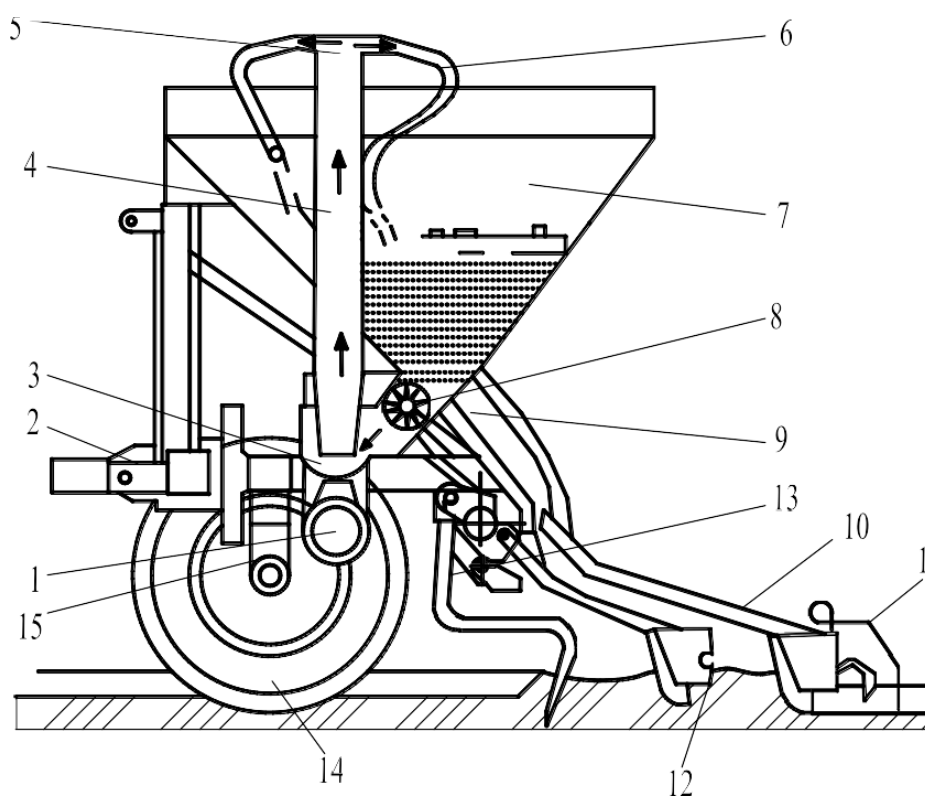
Схема сеялки С-6ПМ2: 1 – вентилятор; 2 – карданный вал; 3 – эжектор; 4 – вертикальный трубопровод; 5 – делительная головка; 6 – семяпровод; 7 – бункер; 8 – высевающий аппарат; 9 – механизм привода; 10 – трубки сошников; 11 – загортачи; 12 – сошники; 13 – рыхлительные лапы; 14 – колеса; 15 – цепная передача
